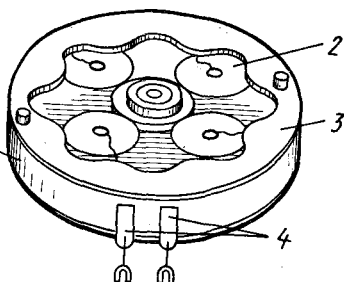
Статор шагового двигателя со встроенными катушками:
